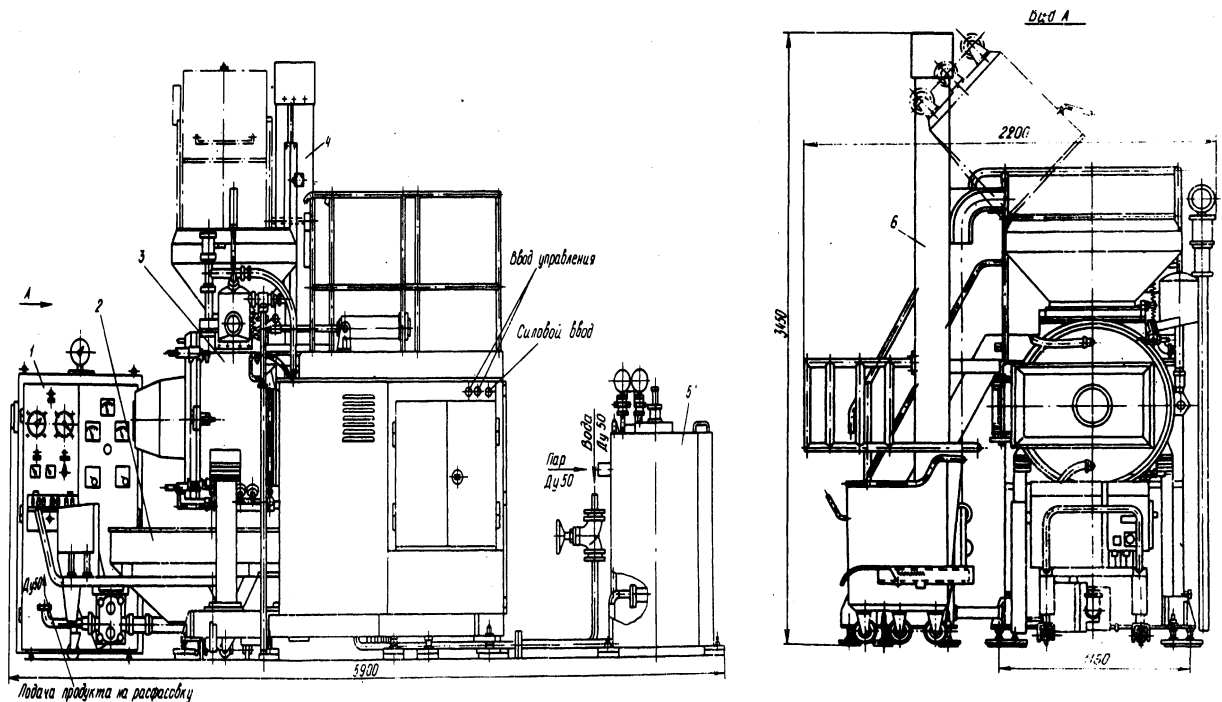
Загальний вид плавильного агрегата марки В2-ОПН;
